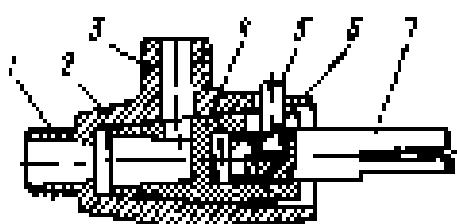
Унифицированный пробковый кран газовой плиты: 1 - штуцер для присоединения к газопроводу; 2 - корпус; 3 - штуцер для присоединения к коллектору; 4 - пробка; 5 - стопорный винт; 6 - пружина; 7 - стержень
